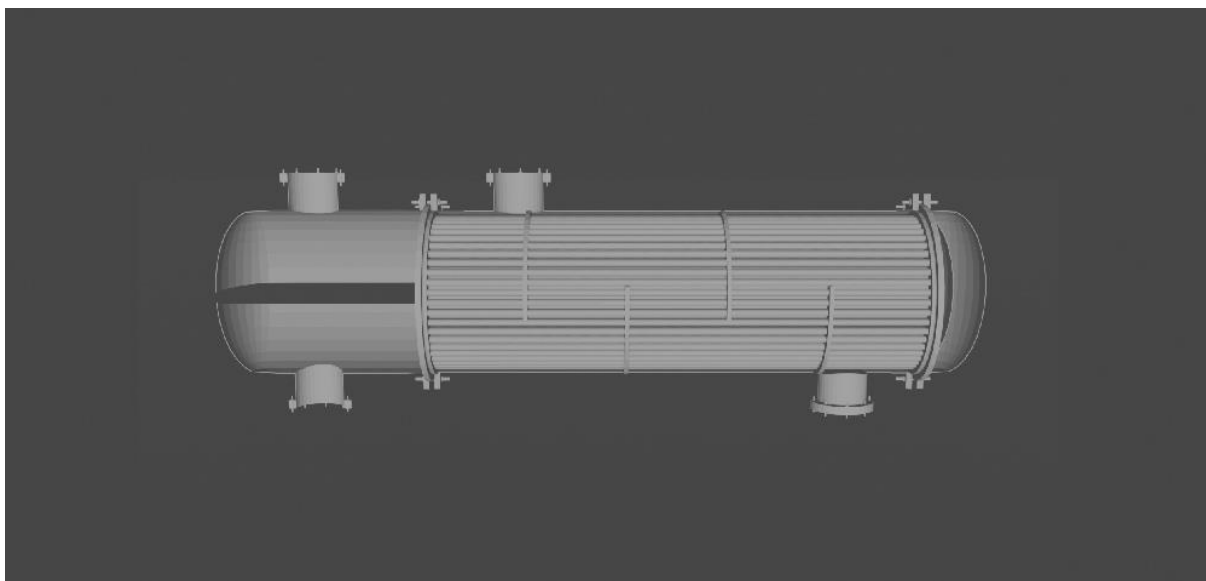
Кожухотрубчатый теплообменник с плавающей головкой в разрезе
